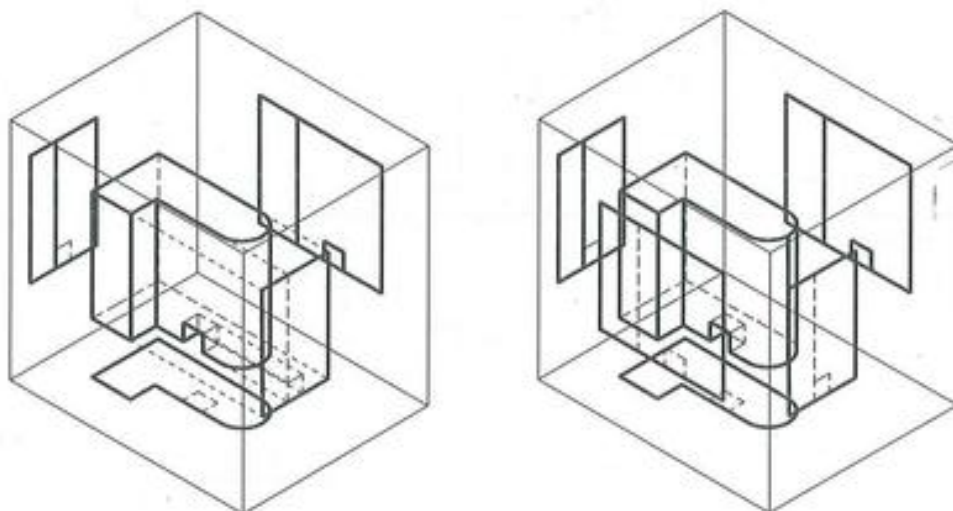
Proyecciones sobre un lateral y el plano anterior del paralelepípedo de proyección.
